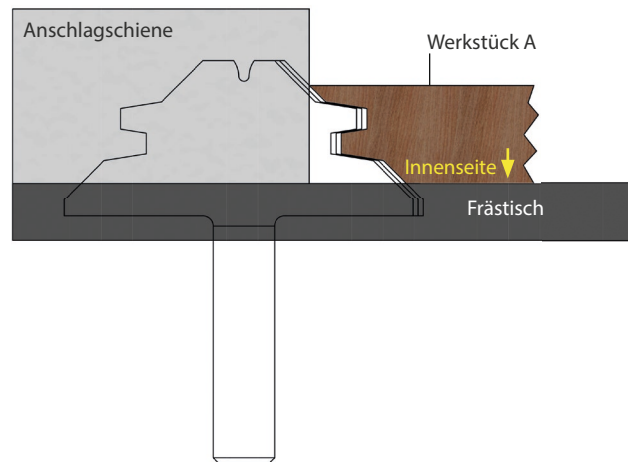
Fräsen des Werkstücks A mit der Innenseite zum Frästisch
